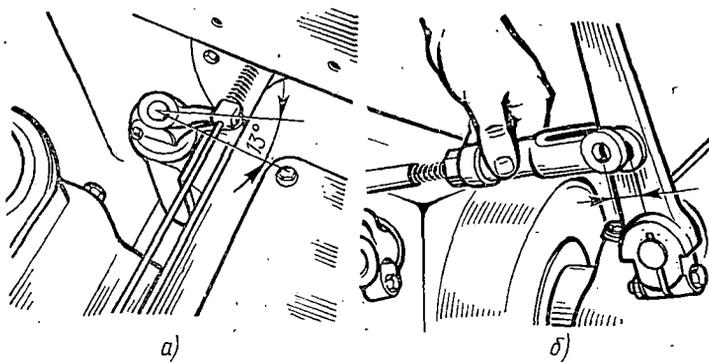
Положение рычагов при регулировке блокировочного механизма коробки перемены передач трактора Т-100М: а — рычага валика блокировки, б — рычага управления муфтой сцепления и тягой валика блокировки
